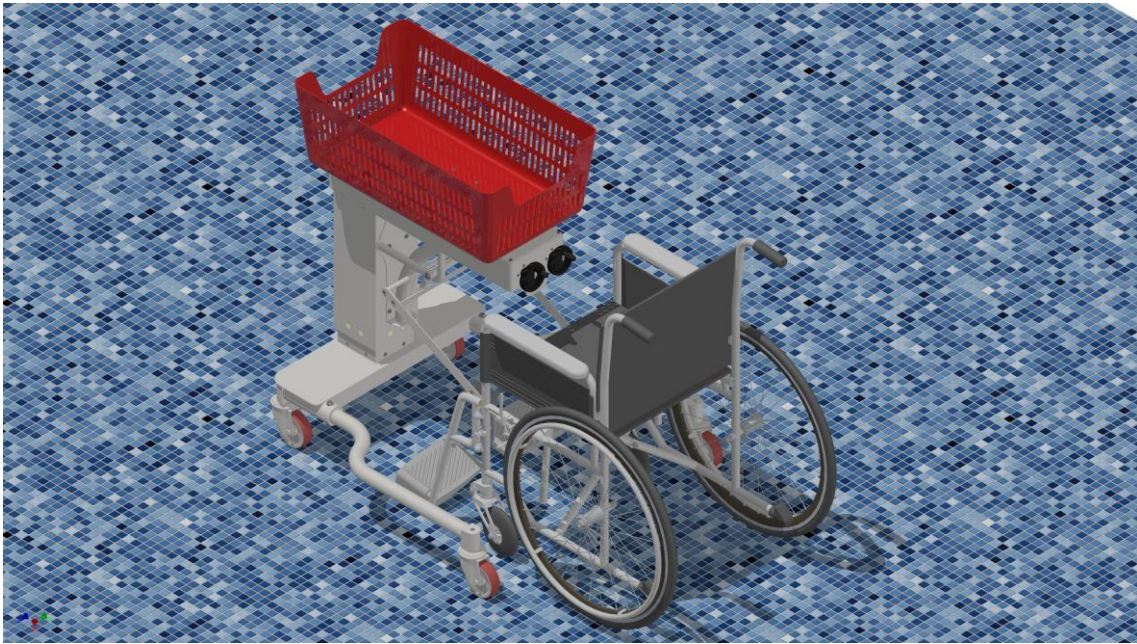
Conjunto carrito-silla de ruedas. Vista isométrica.
